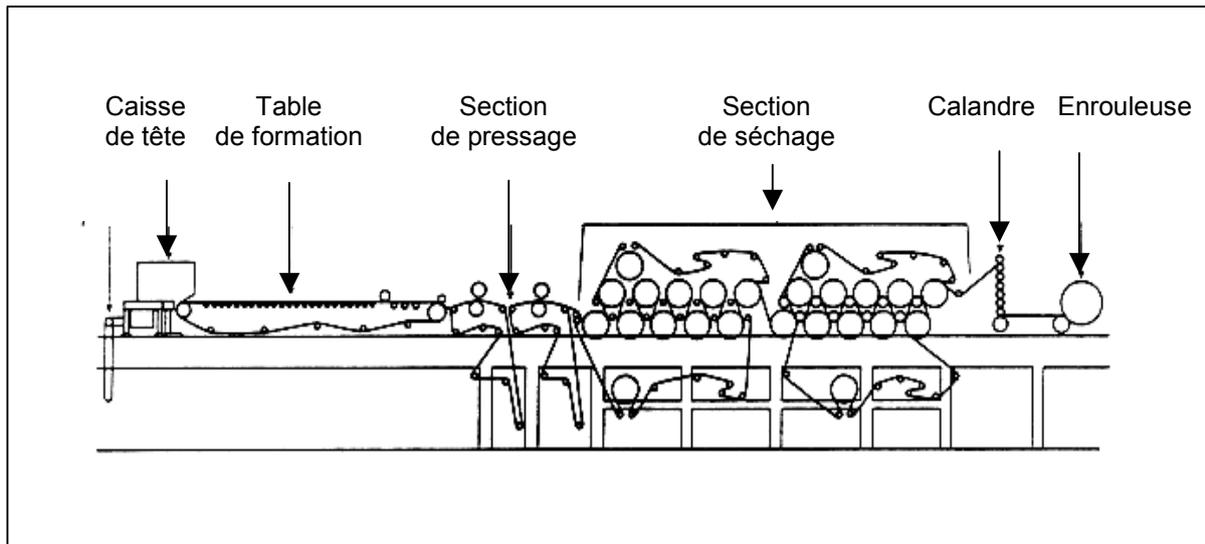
Ligne de production de papier équipée d'une machine de type Fourdrinier
